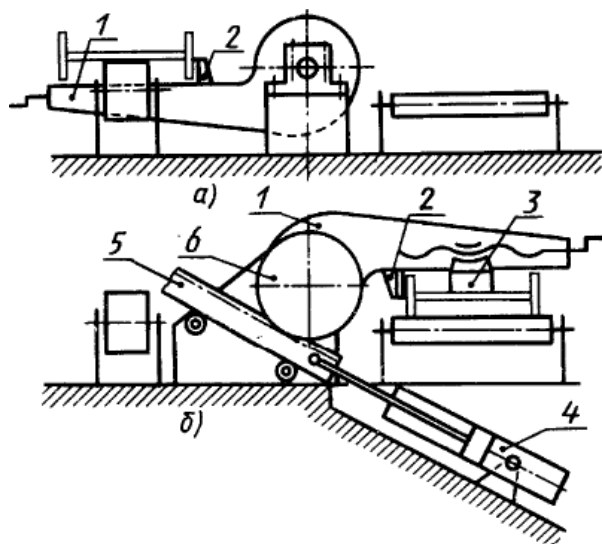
Конструктивная схема магнитного кантователя на 180°
